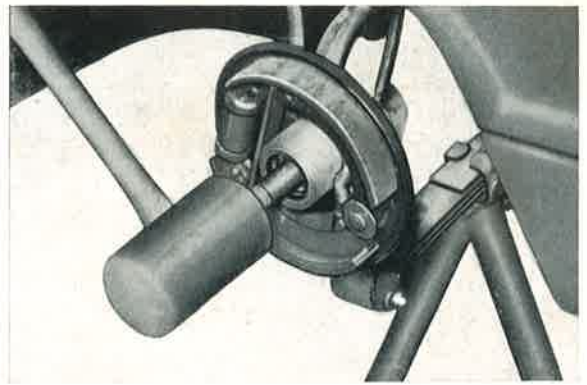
Mit einem Gummihammer wird die äußere Gelenkwelle nach innen aus d. Lagerung herausgeschlagen.
